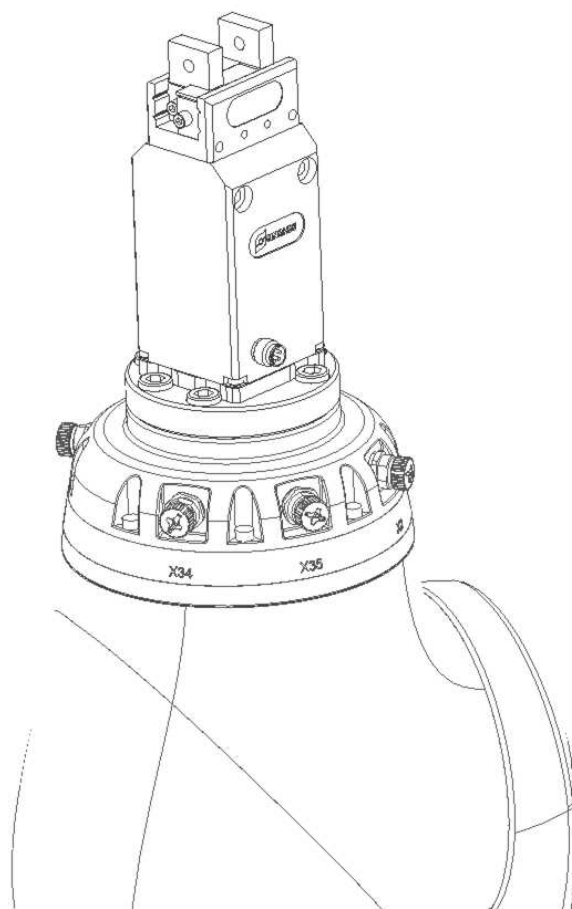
Přípojovací příruba a robot LBR iiwa 14R820
